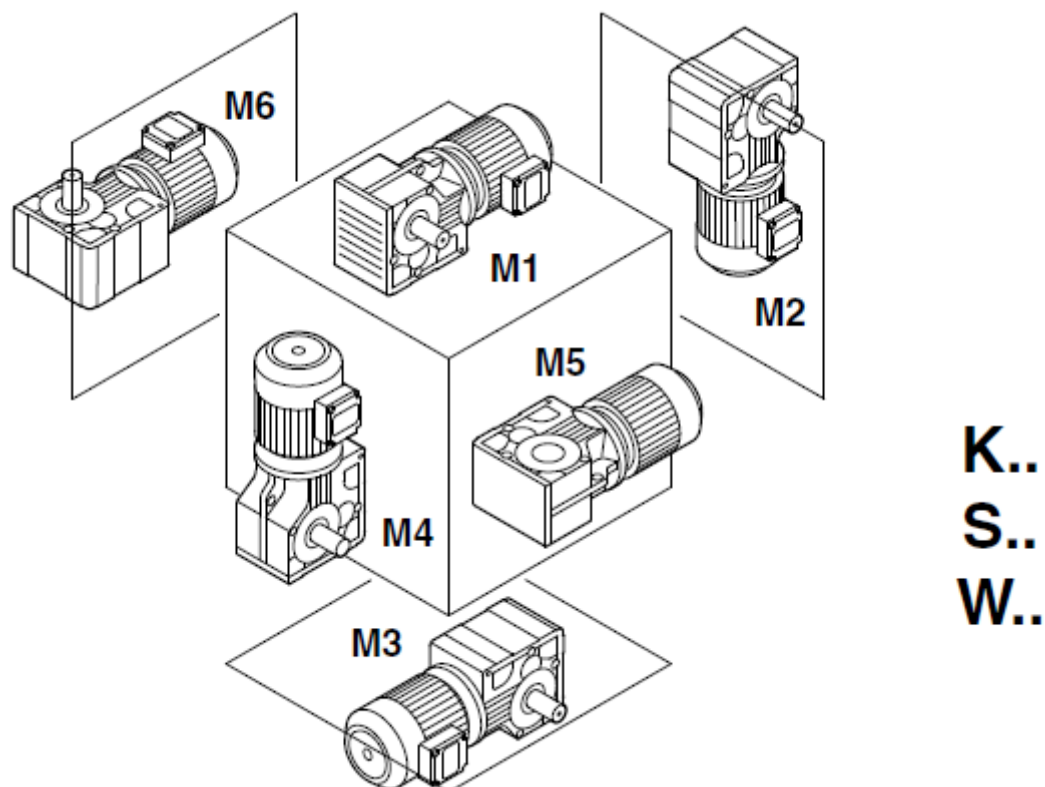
Posiciones del montaje del motorreductor [SEW, 2009].
